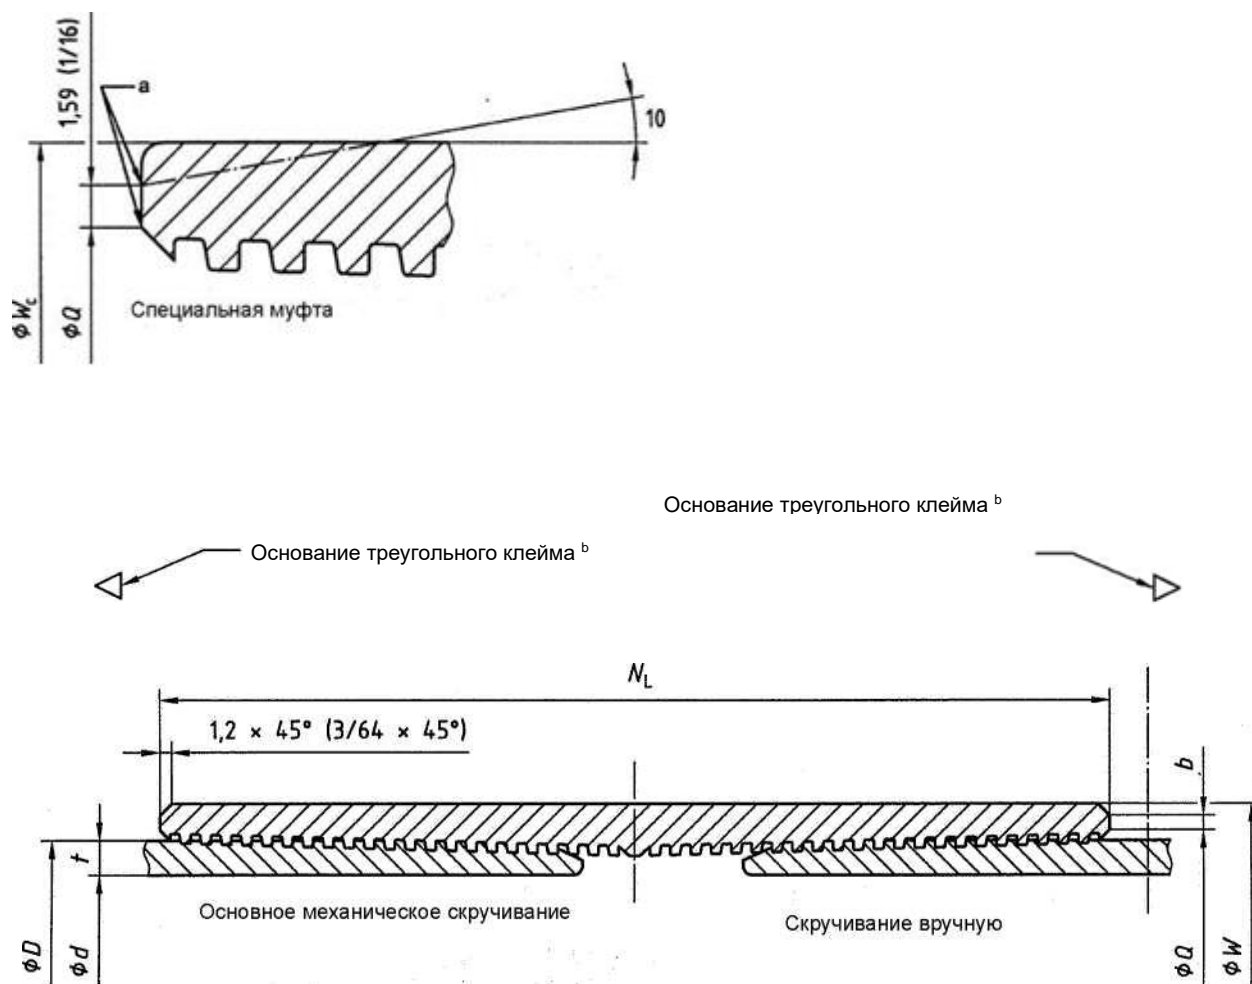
Обсадные трубы и муфты с короткой закругленной резьбой
